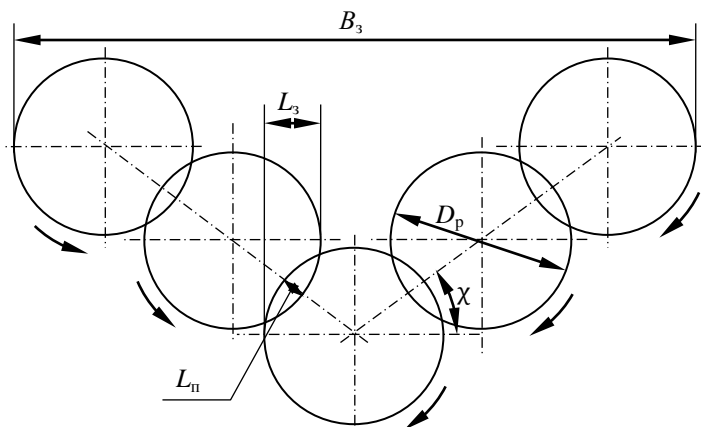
Схема режущего аппарата пятироторной косилки разрабатываемой конструкции
